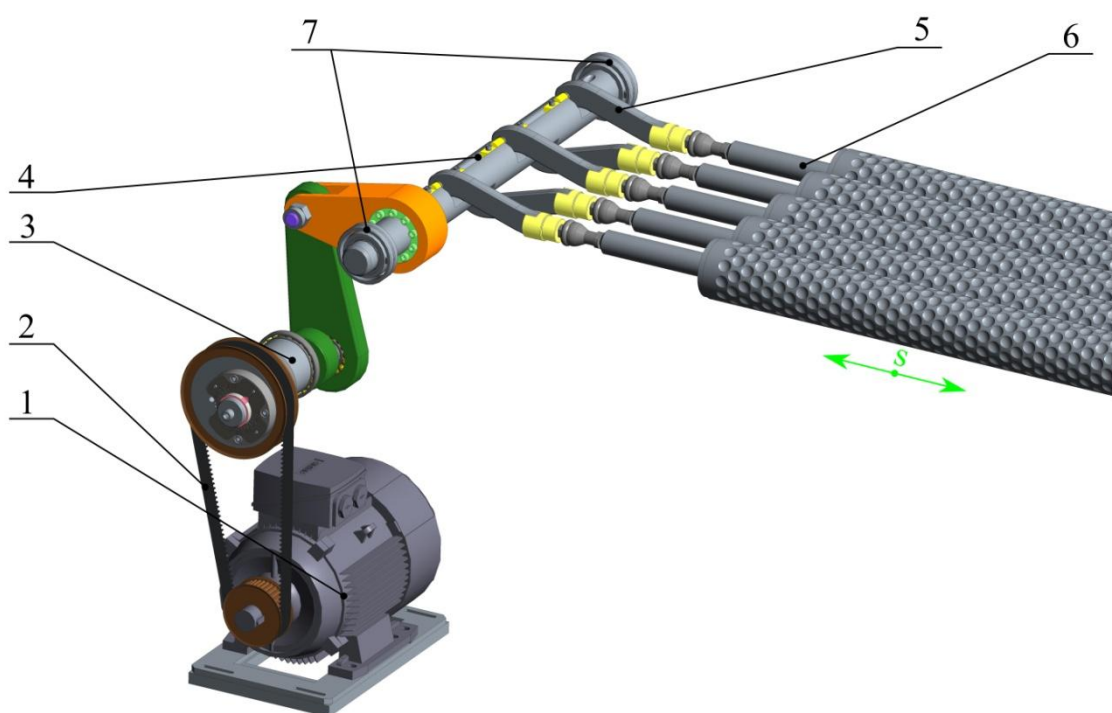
Zařízení pro změnu axiálního zdvihu CAD model
